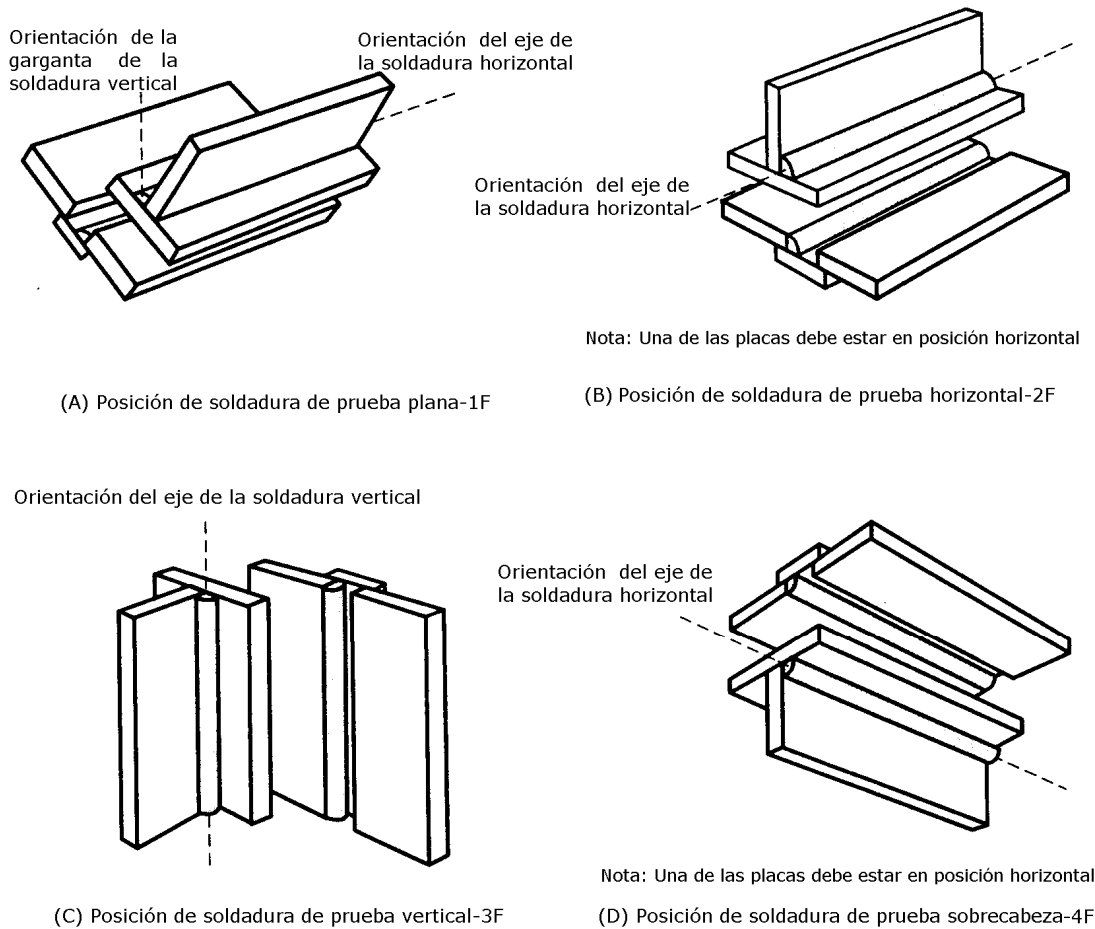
Posiciones de prueba básicas, para soldaduras de filete en placa
